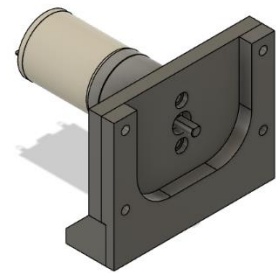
Isométrico soporte motor escuadras y placa motor ensamblados
